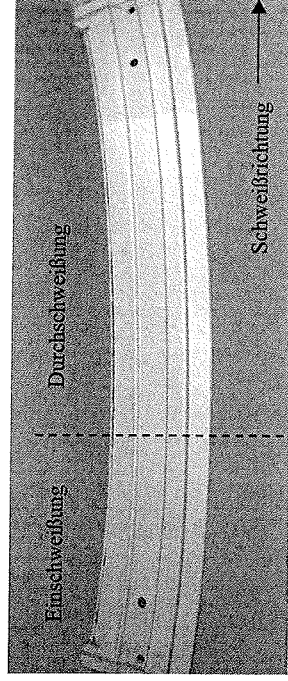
Rückansicht eines geschweißten Dachquerträgers (Basis für Signale aus Bild 5-12).
